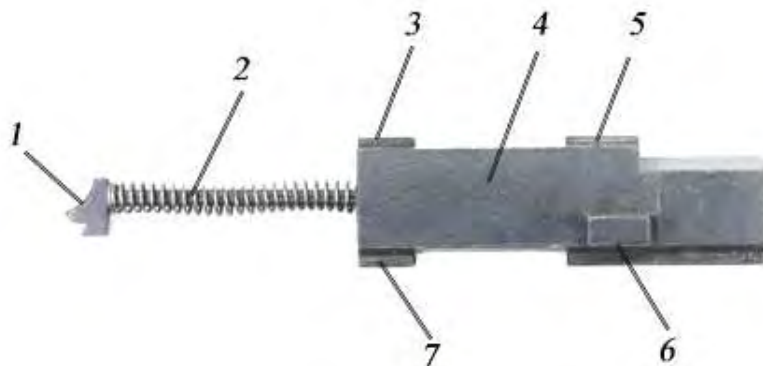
Замедлитель с направляющим стержнем: 1 – выступ для соединения с рамкой; 2 – пружина замедлителя с направляющим стержнем; 3, 5, 6, 7 – направляющие выступы; 4 – замедлитель
